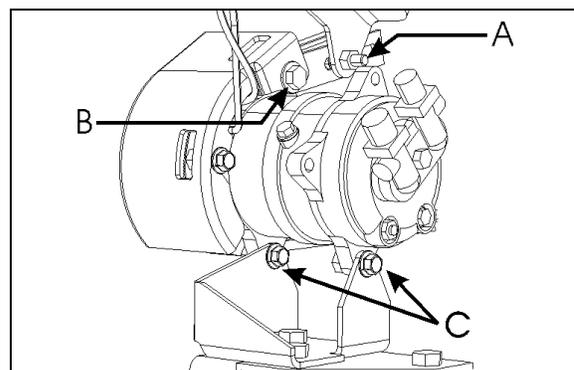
DÉMONTAGE OU INSTALLATION DU COMPRESSEUR
